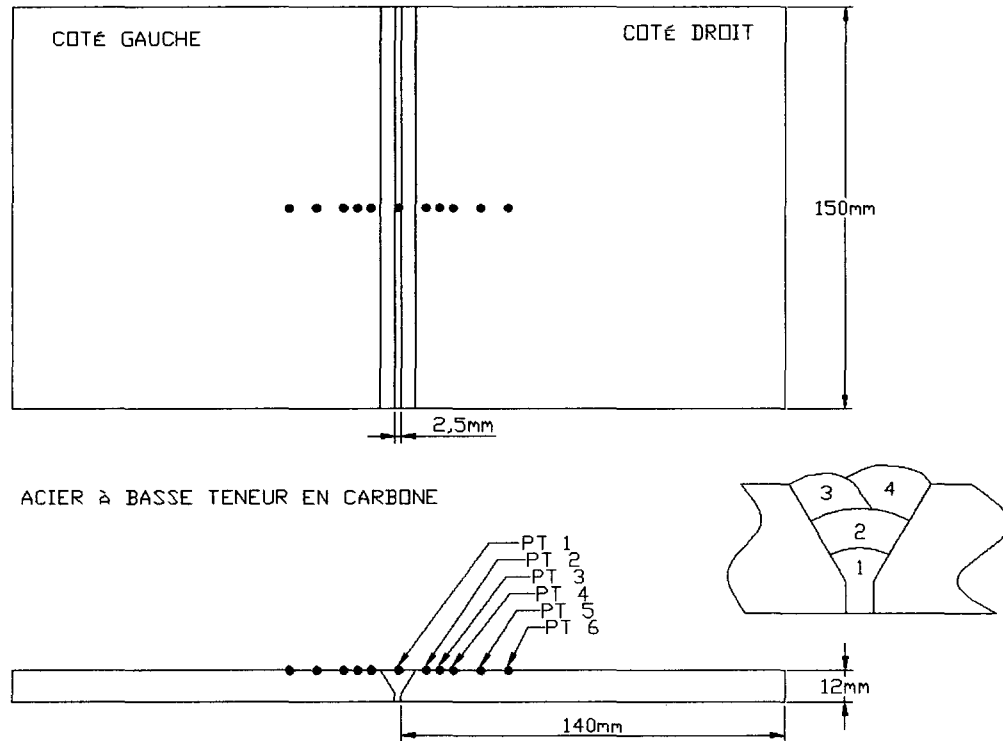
Détails dimensionnels de l'essai de Murugan [2]
